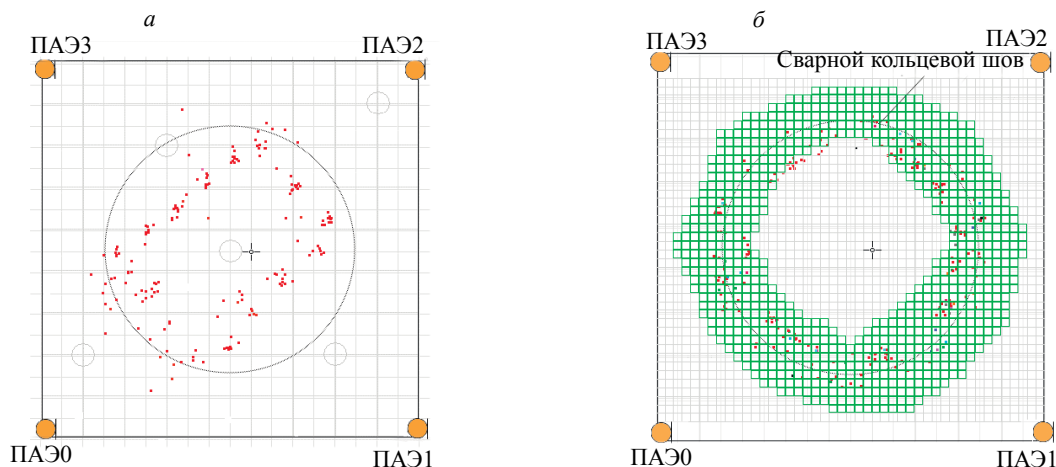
Локация сигналов АЭ при калибровке зоны контроля кольцевого сварного шва:
